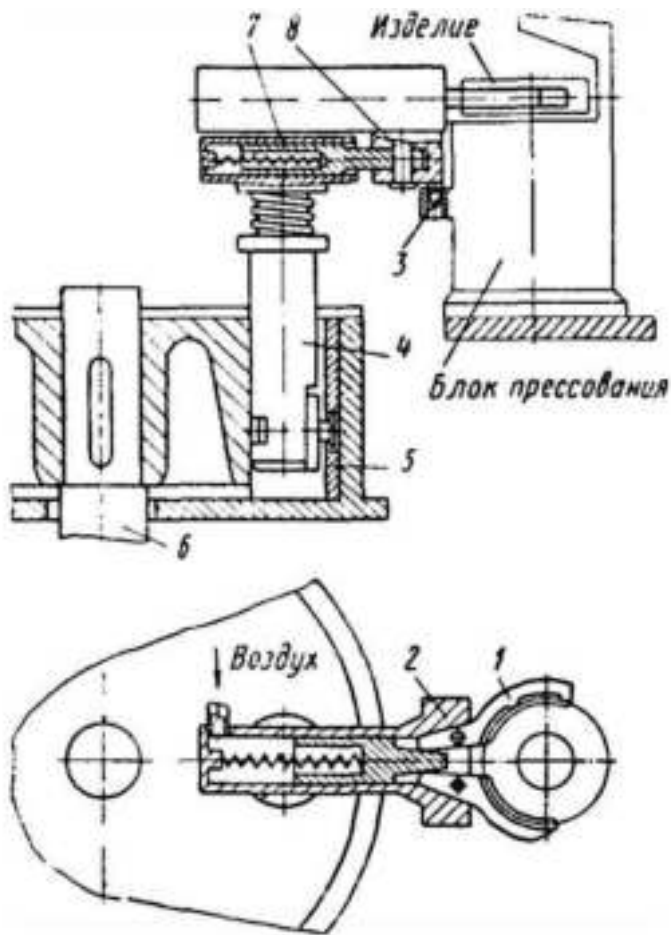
Транспортный ротор: 1 – захватные органы; 2 – пневмоцилиндр; 3 – фиксирующий штырь; 4, 7 – ползуны; 5 – цилиндрический кулачок; 6 – роторный вал; 8 – ось вращения пневмоцилиндра
